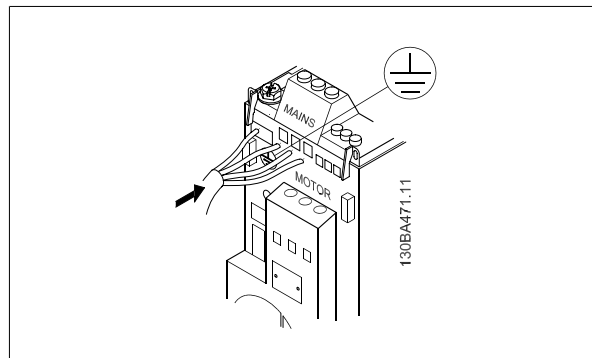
Montaje de los cables de red eléctrica y toma de tierra.
